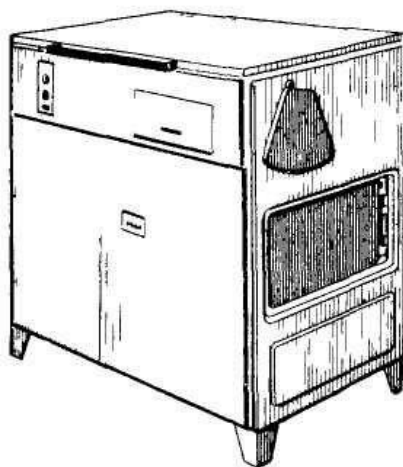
Установка ОРГ-4990Б-ГОСНИТИ для миття деталей
